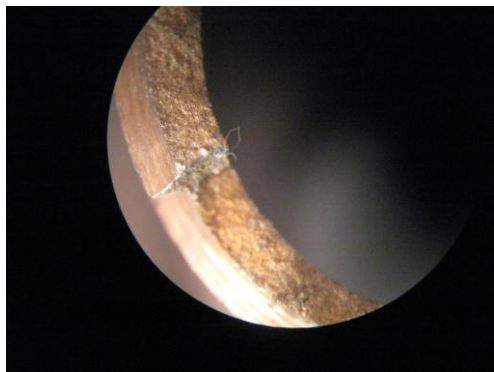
Шлакове включення на поверхні злому корпусу штуцера
